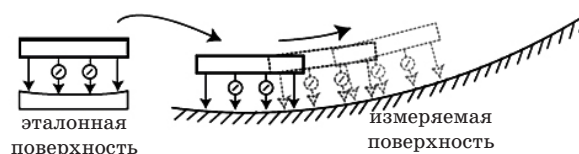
Сферометр для контроля профиля асферической поверхности.
